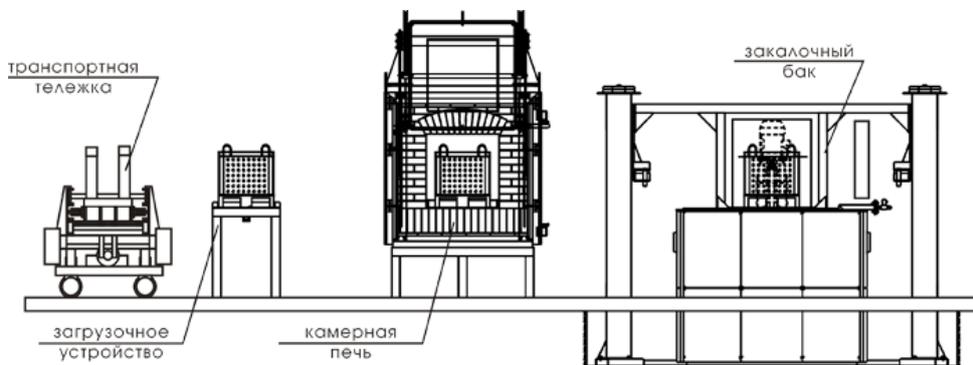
Закалочный агрегат на базе камерной печи СНО-7.12.7/10
